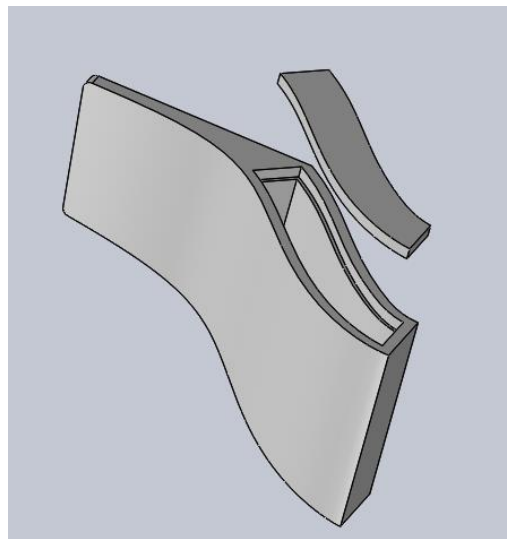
Vista explosionada del subensamblaje unión cuerpo brazo izquierdo. [2]
